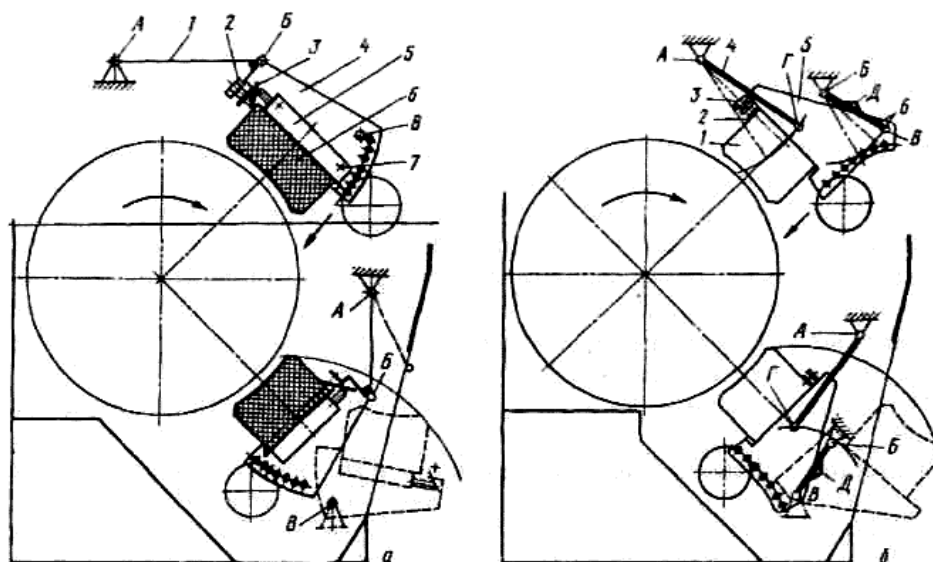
Схема подвески дек: а - станка 2ДШС-3А: 1 - рычаг; 2,7 - болты; 3 - нажимная планка; 4 - декодержатель; 5 - обойма; 6 - дека; б - станка 2ДШС-3Б: 1 - дека; 2 — нажимная планка; 3 - болт; 4, 6 - рычаги; 5 - декодержатель.
